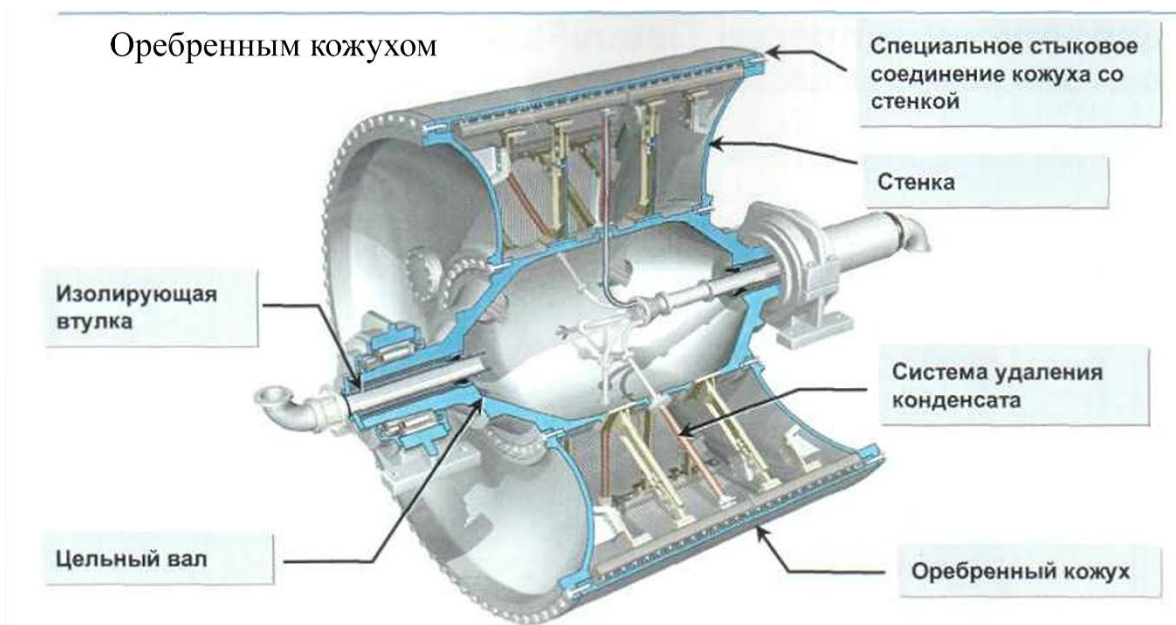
Двухслойный сушильный цилиндр (янки-цилиндр) для выработки санитарно-гигиенической бумаги
